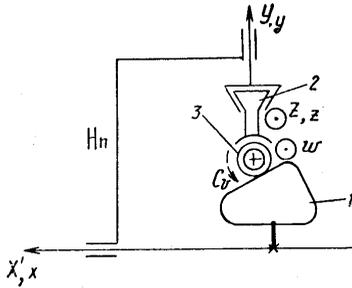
КТС в вертикально-фрезерного станка с ЧПУ:
